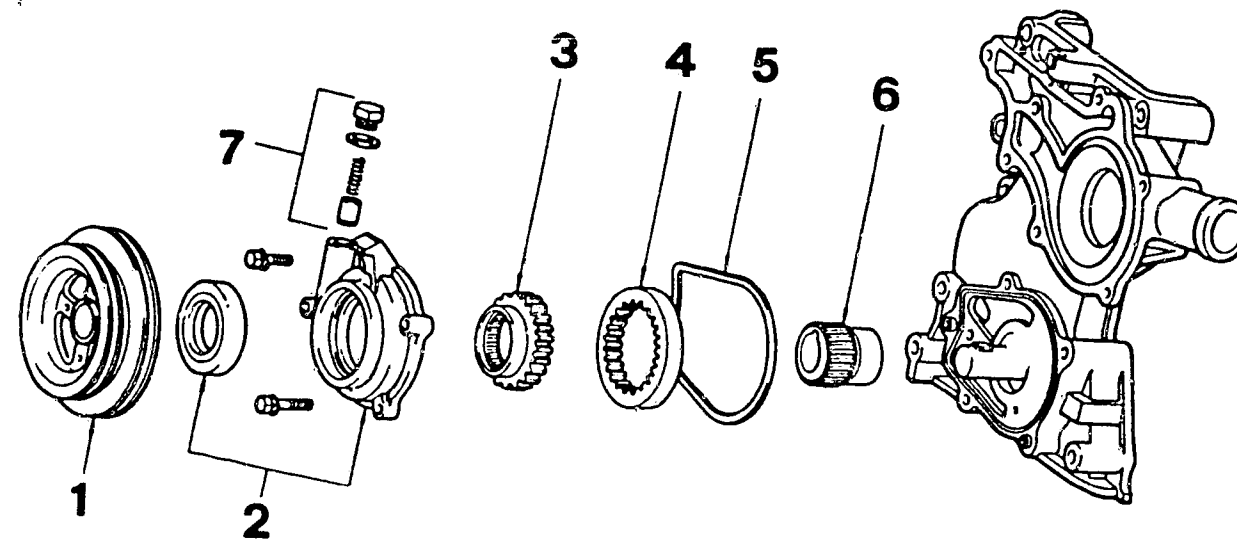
Motor 21R/21R-C: Die Numerierung der einzelnen Teile der Ölpumpe entspricht der Ausbaureihenfolge. 1 Keilriemenscheibe der Kurbelwelle – 2 Gehäuse der Ölpumpe – 3 Pumpenantriebszahnrad – 4 Pumpeninnenzahnrad – 5 O-Ring – 6 Antriebsverzahnung der Ölpumpe – 7 Überdruckventil-Einheit.
